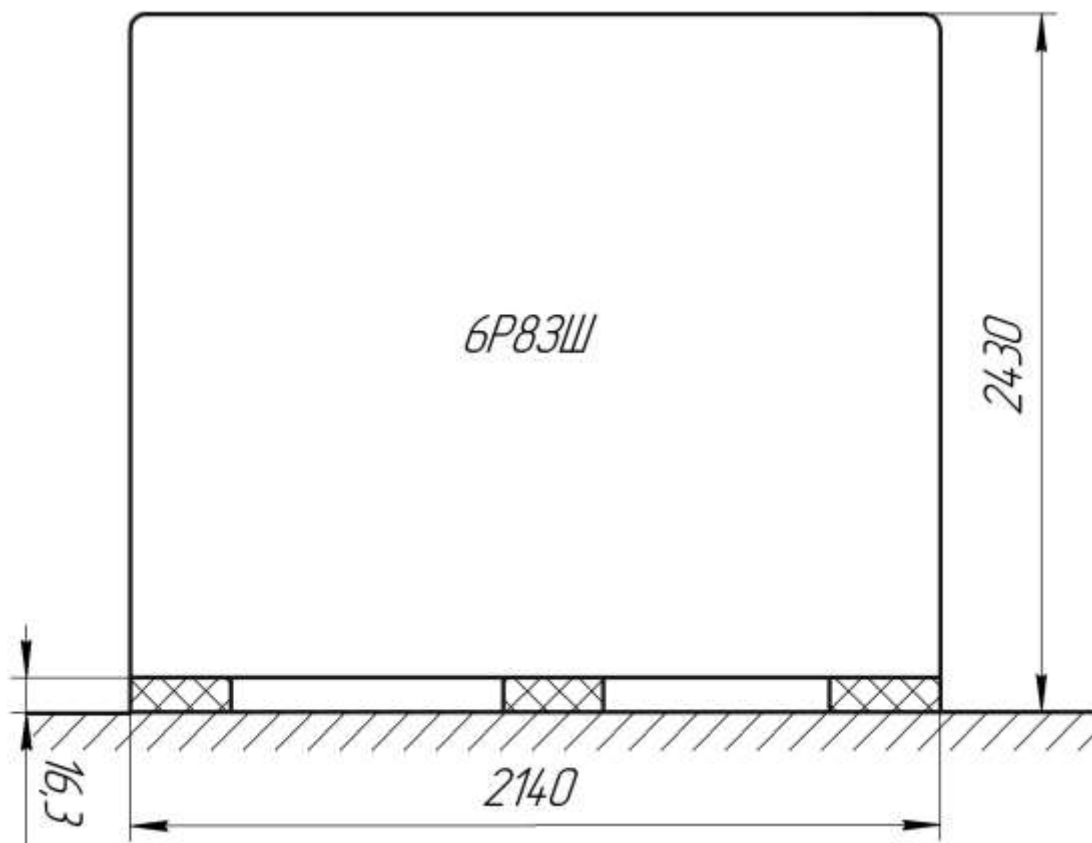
Схема віброізоляції фрезерного верстату 6P83Ш
